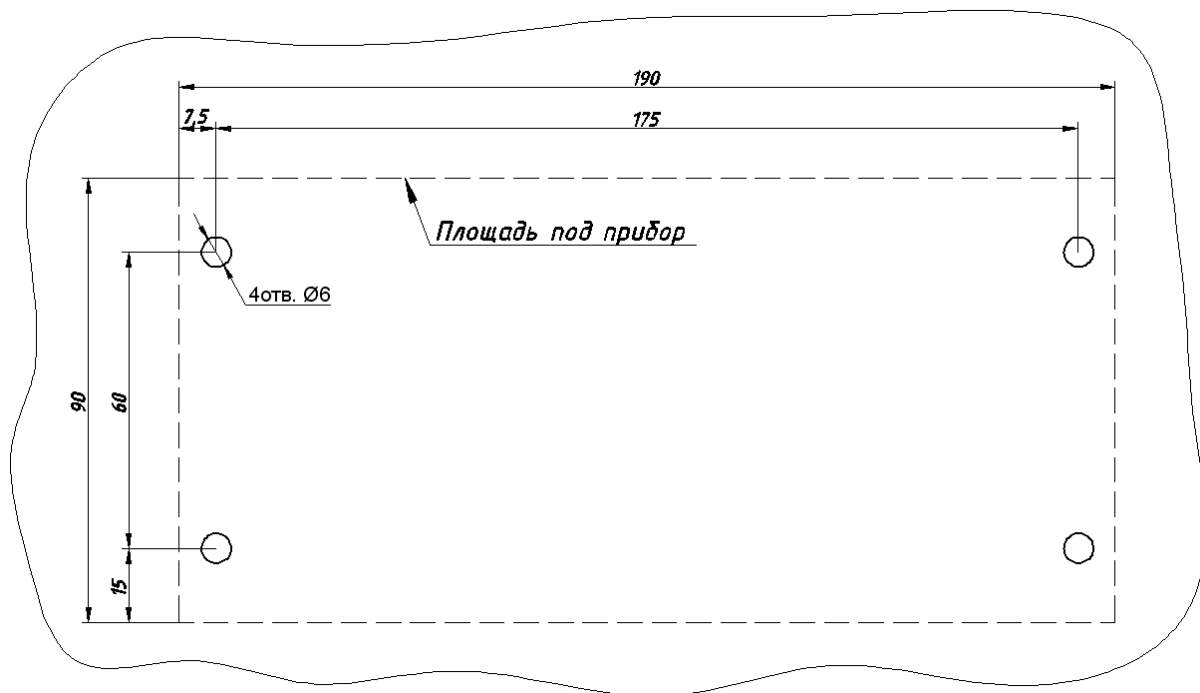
Посадочные размеры для прибора Ф1791.2
